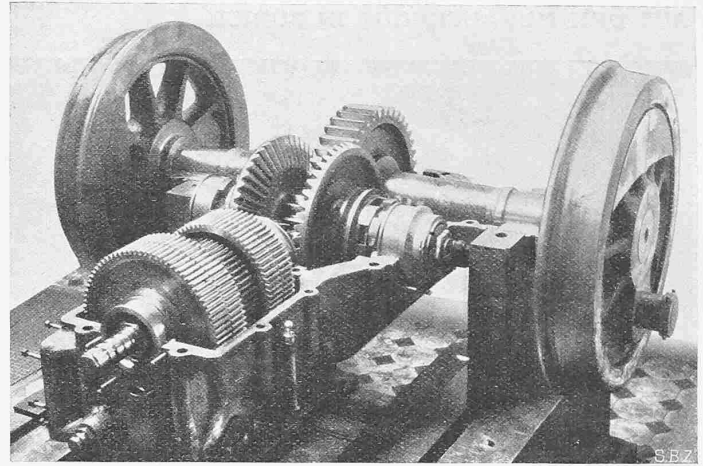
Stufengetriebe mit Oeldruckschaltung, und Wendegetriebe.
